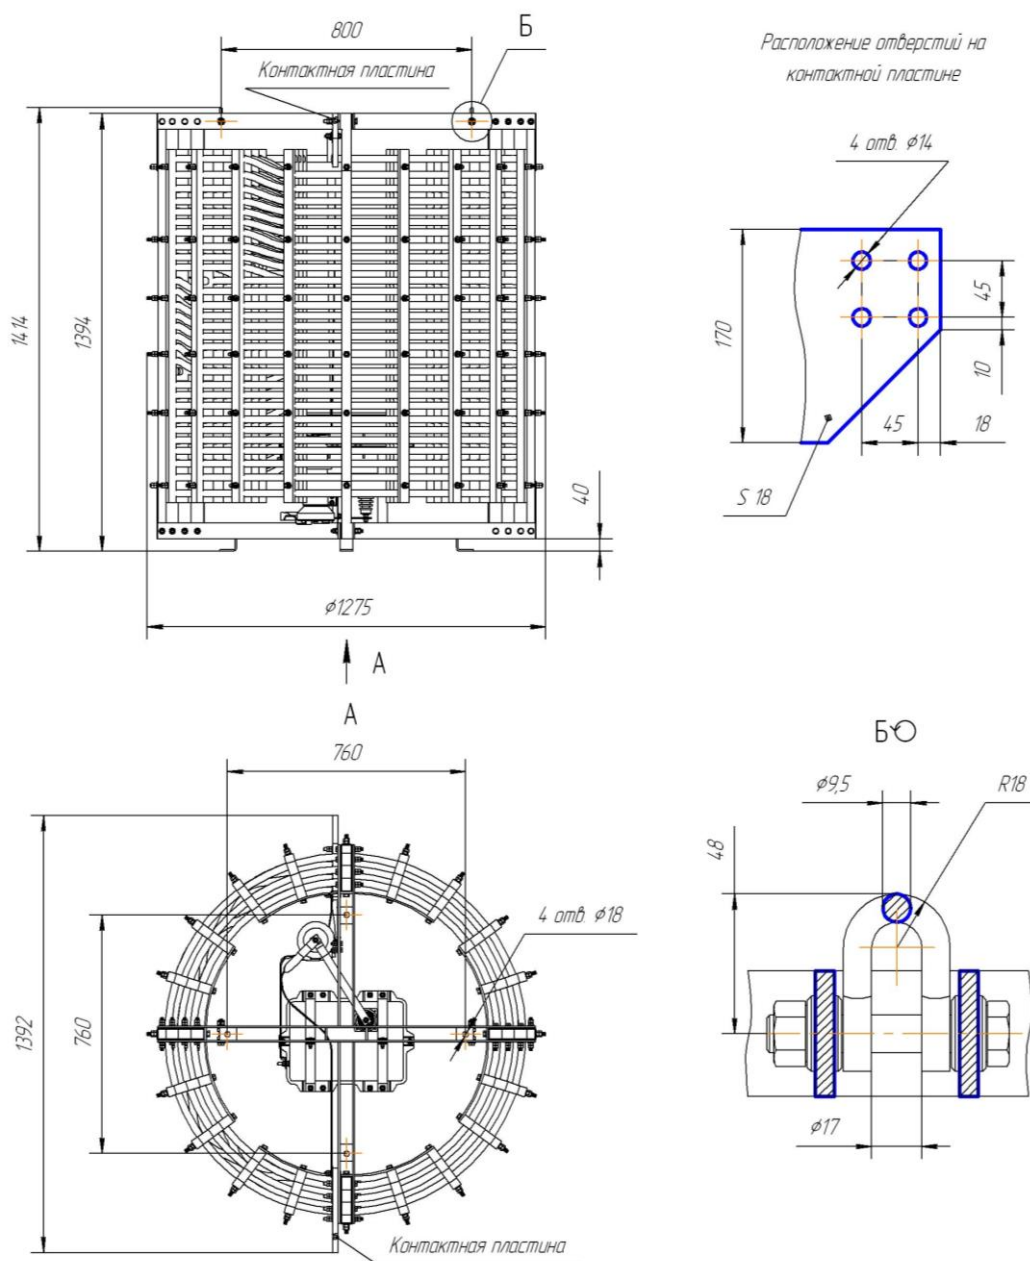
Габаритный чертеж ВЗ–630–0,5.
